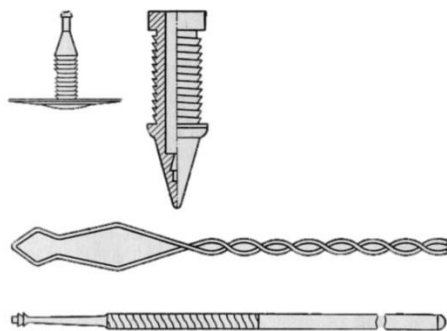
Приспособления для ремонта проколов: а — резиновый грибок; б — полая резиновая пробка; в — проволочная петля; г — стержень для вставки пробки
